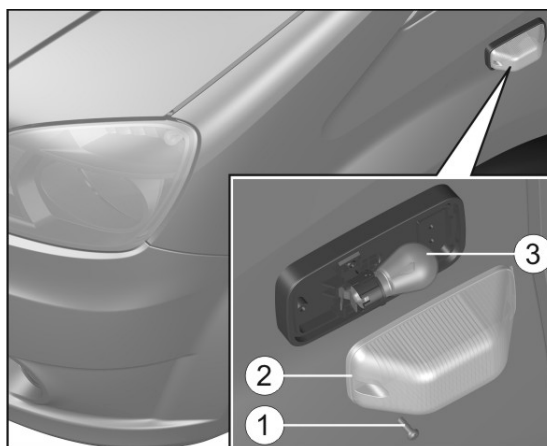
Указатель поворота боковой: 1 – винт; 2 – рассеиватель; 3 - лампа
